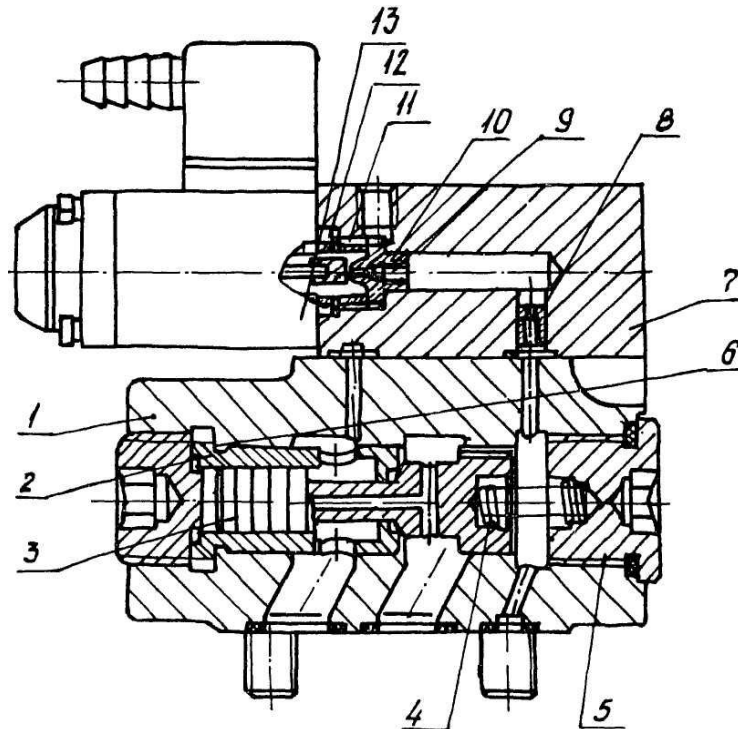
Конструкція запобіжного клапана типу МПКПД: 1 – корпус; 2 – втулка; 3 – запірно-регулюючий елемент; 4 – пружина; 5, 6 і 11 – пробки; 7 – корпус керуючого клапана; 8, 10 – демпфери; 9 – сопло; 12 – пропорційний електромагніт; 13 – втулка, яка виконує функцію заслінки
